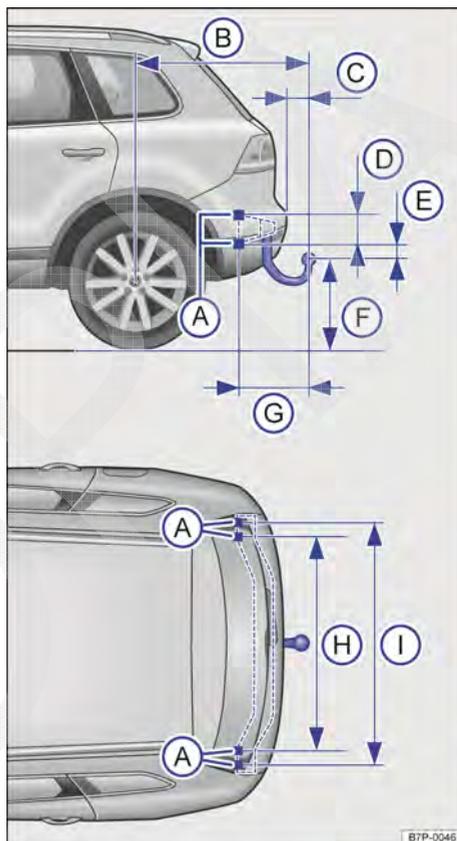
Dimensões e pontos de fixação para instalação posterior de um dispositivo de reboque.
